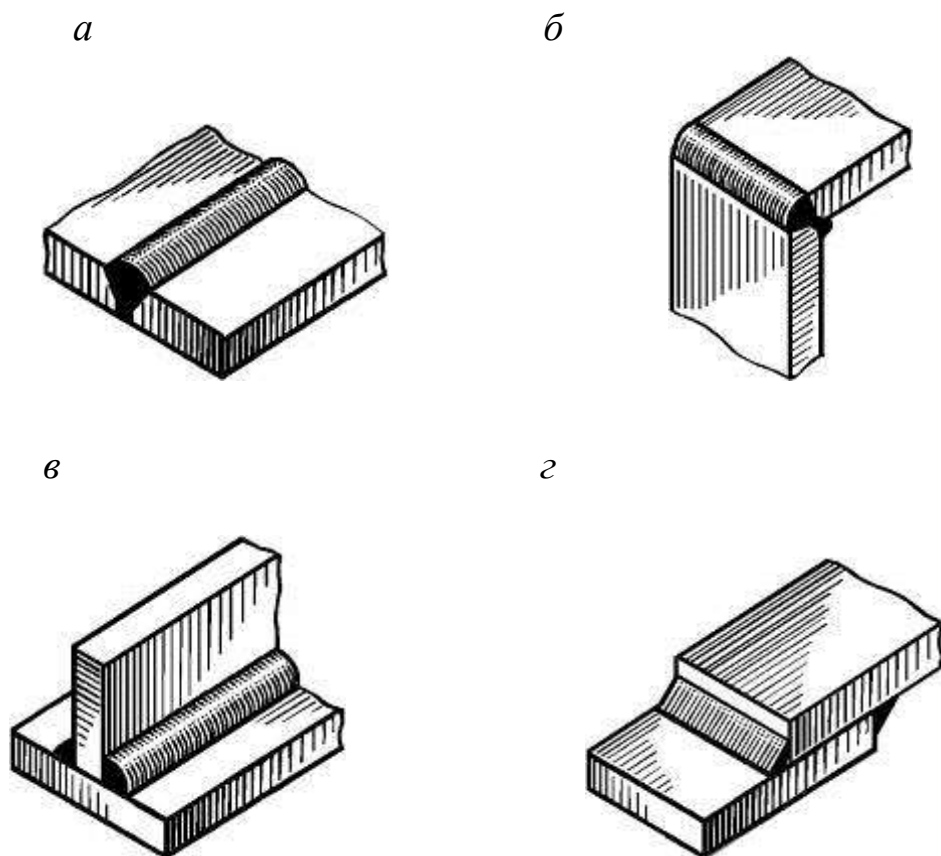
Сварные соединения: *а* – стыковое; *б* – угловое;
